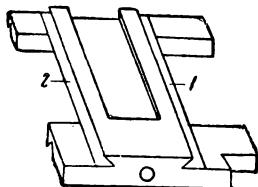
Проверка шабровки плоских направляющих для каретки суппорта.
